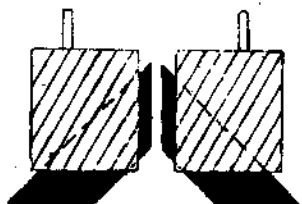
Устройство зажимов для угловой сварки встык.
